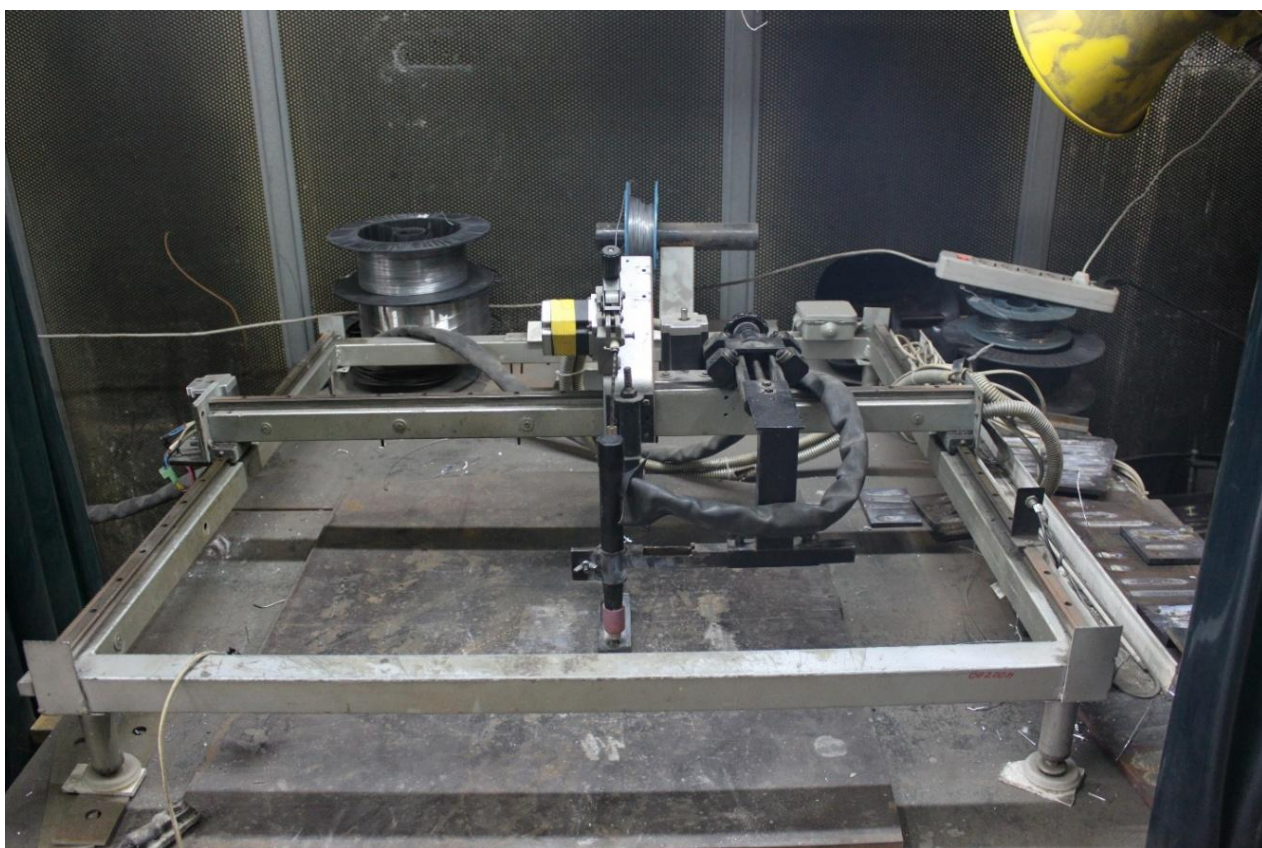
Внешний вид установки для автоматической аргонодуговой наплавки с подачей присадочной алюминиевой проволоки
